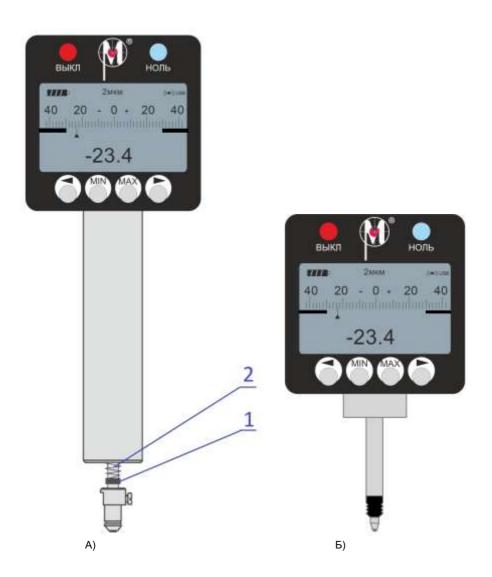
Внешний вид головок. А) головка ИГЦ; Б) головка ИГЦМ 1. Шайба регулировки измерительного усилия; 2.Пружина
